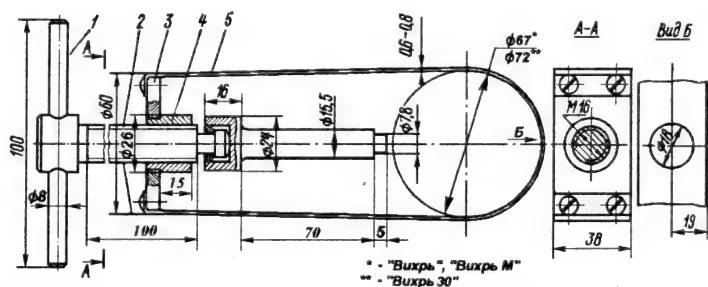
Выжимное приспособление для выпрессовки и запрессовки поршневого пальца
